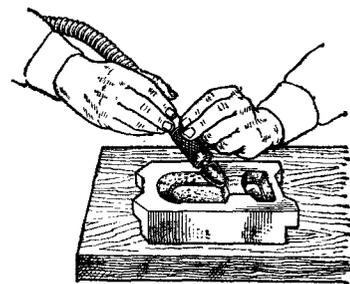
Прием шлифования поверхностей абразивными фасонными головками с приводом от гибкого вала
